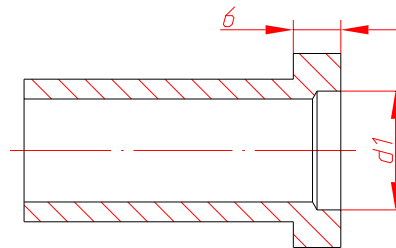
Ниппель типа ...-НП3-Н-18х2,5/24-6. Общий вид
